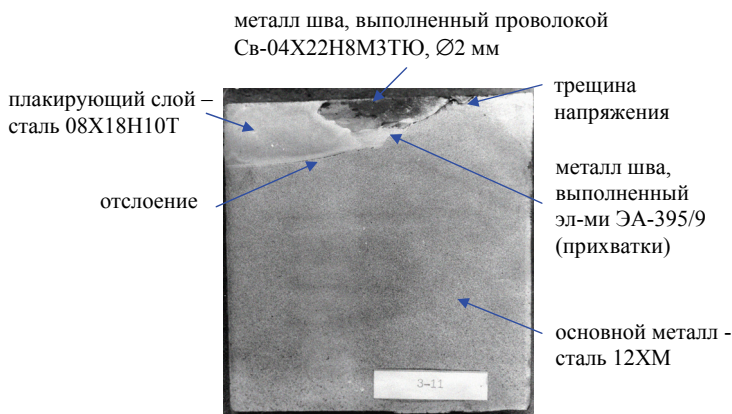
Макроструктура лакированного листа в месте сварного шва пакета (полуавтоматическая сварка в CO_2)
